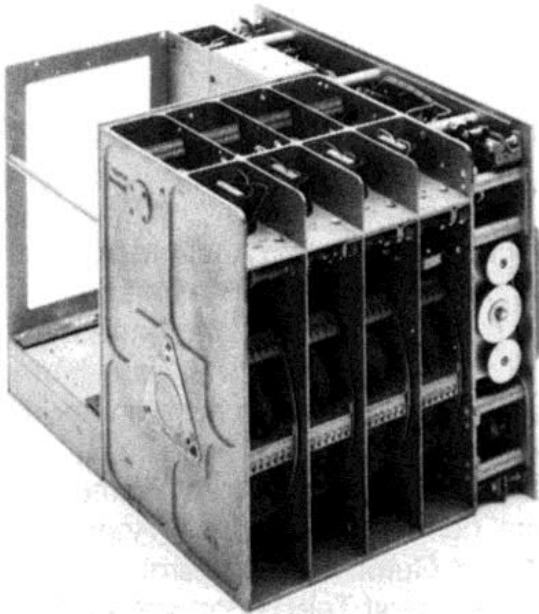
Seitenansicht von links hinten. Abdeckbleche Chassis entfernt.
